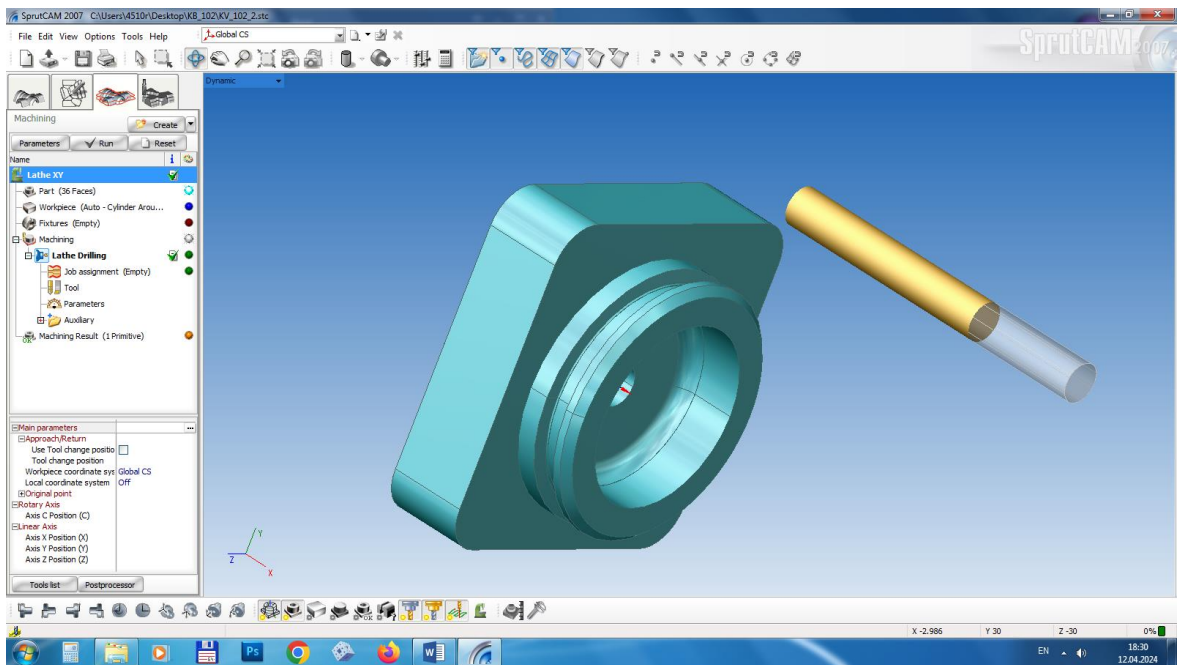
Інструмент і деталь після обробки на верстаті
